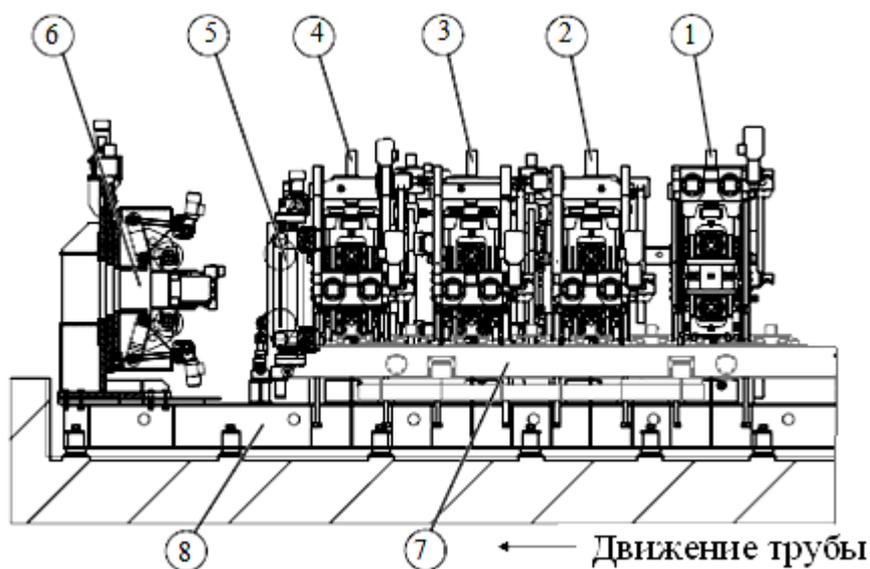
Схема калибровочного стана на ТЭСА 127-426 в ЗАО «Северсталь ТПЗ - Шексна»: 1 - калибровочная клетка №1; 2 - калибровочная клетка №2; 3 - калибровочная клетка №3; 4 - калибровочная клетка №4; 5 - клетка с бочкообразными валками; 6 - турголовка; 7 - сменная рама; 8 - станина
